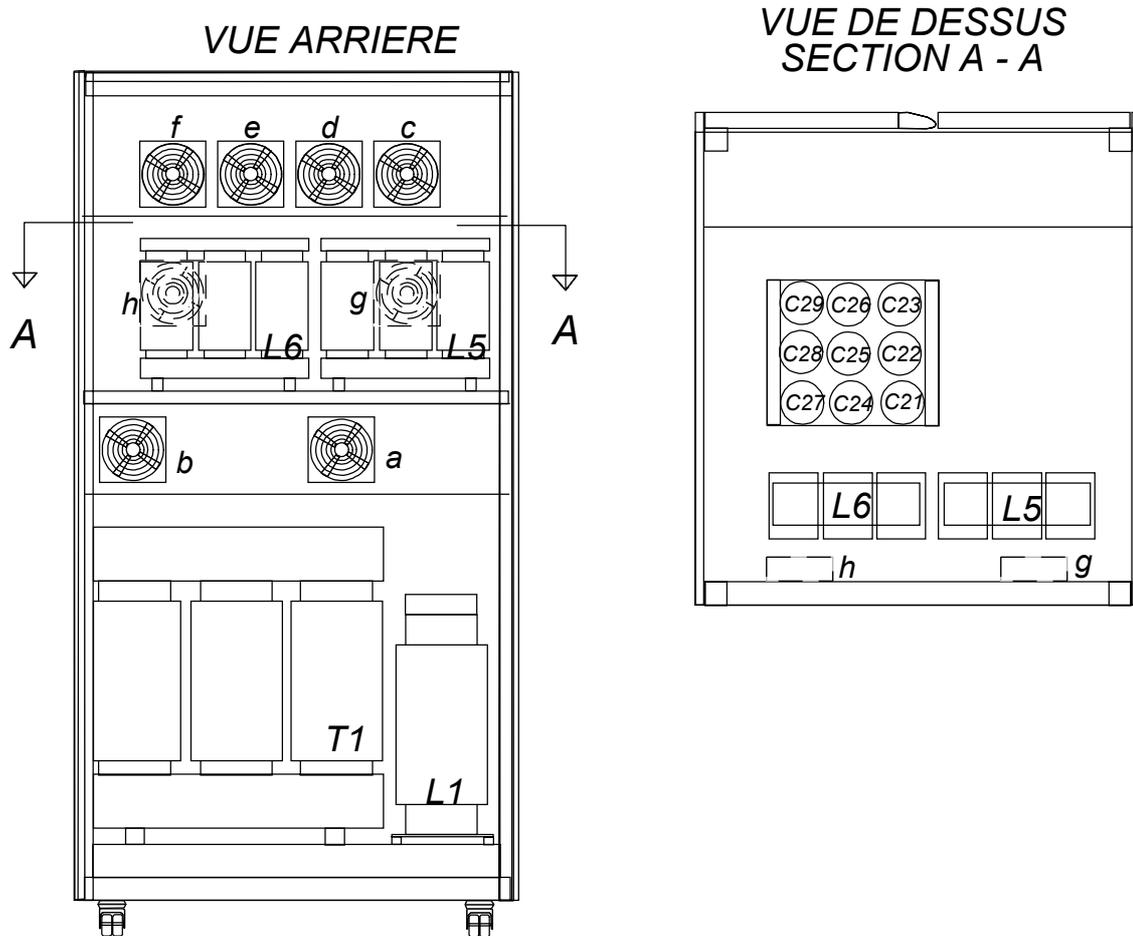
O. Emplacement des pièces du filtre des harmoniques
